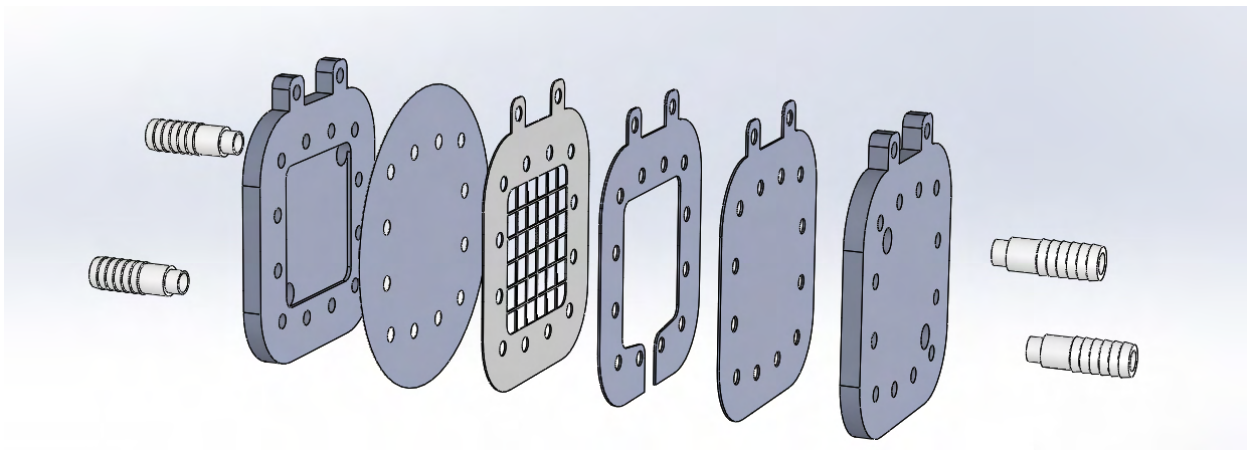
Desenhos esquemáticos das partes do módulo AGMD que foram fabricados via impressão 3D
